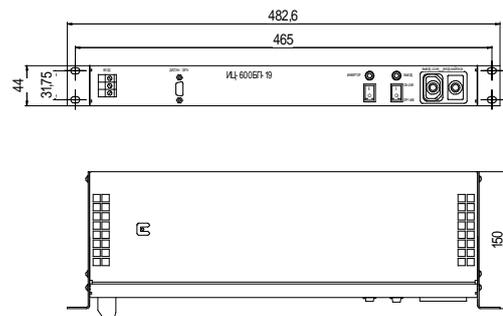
Габаритный чертеж ИЦ-600БП-19
